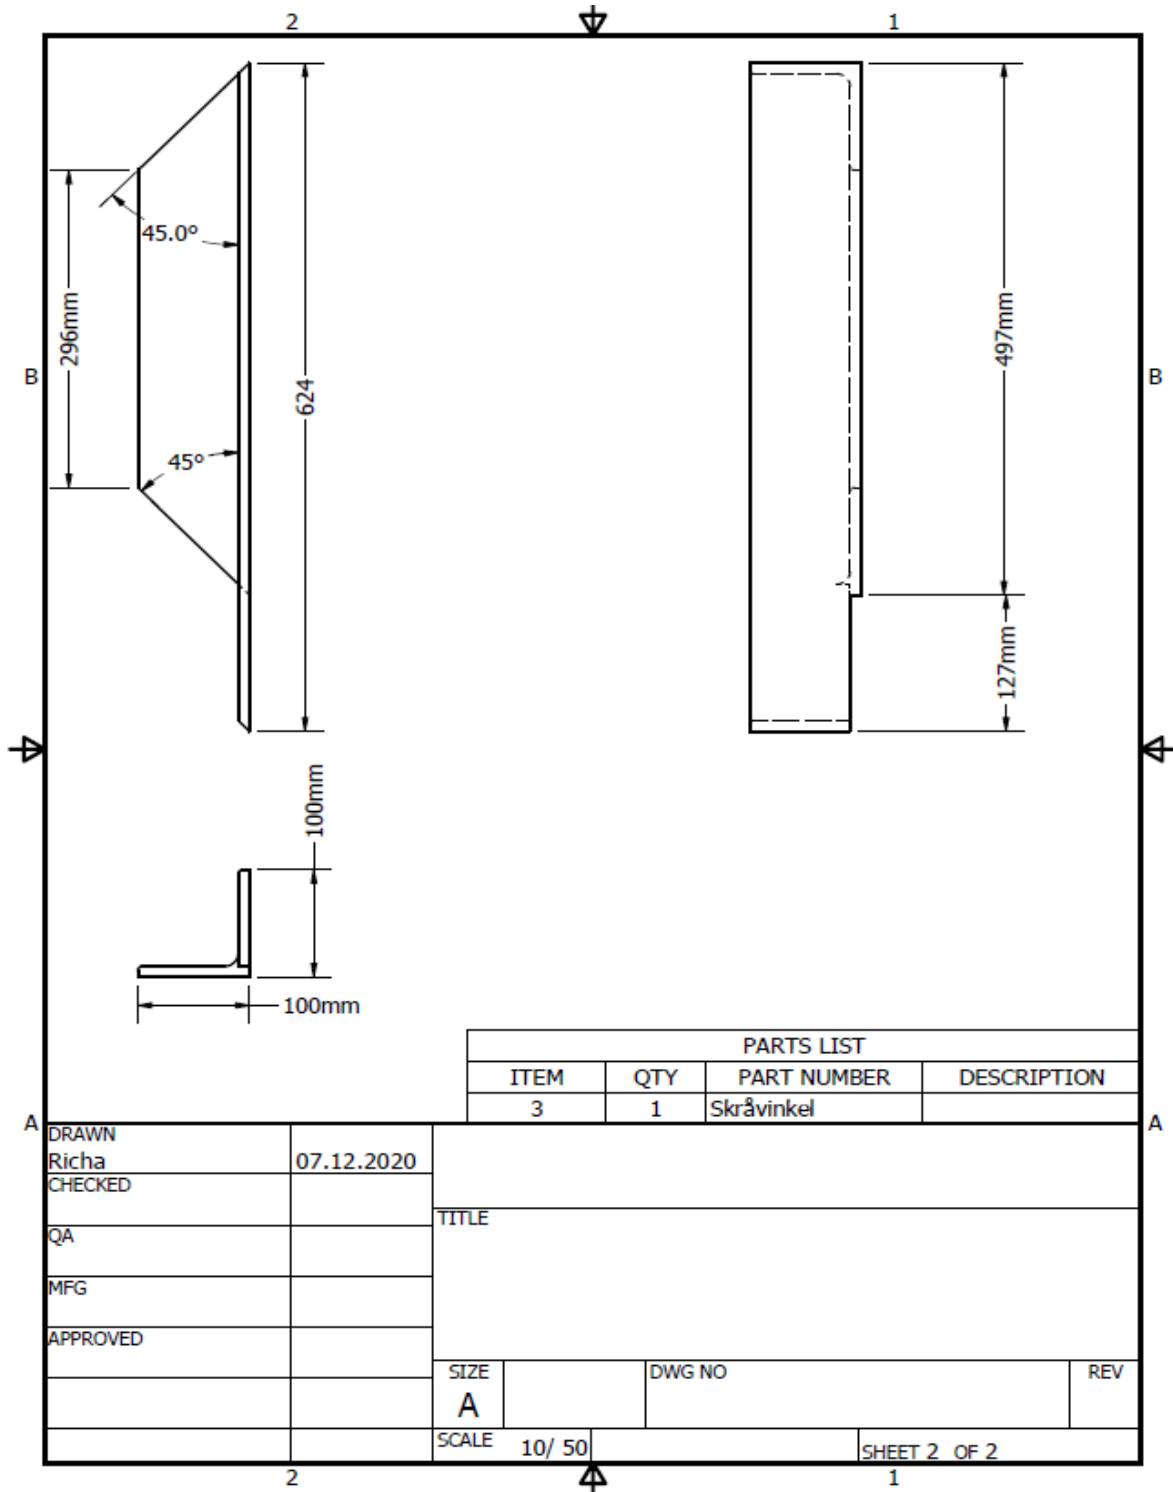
sammenstillingstegning venstreside korreksjon: alle boltehull skal være 20mm
